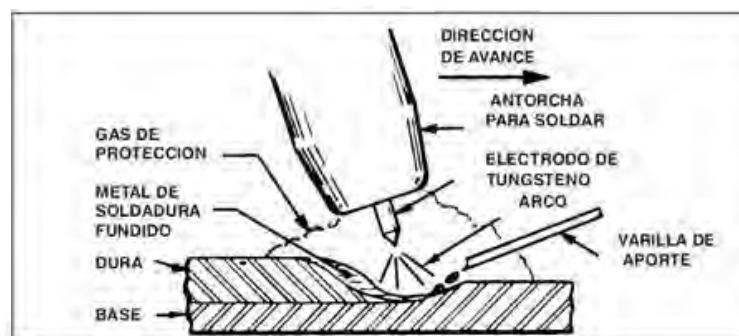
1 Soldadura de arco con atmósfera de gas inerte (TIG)
